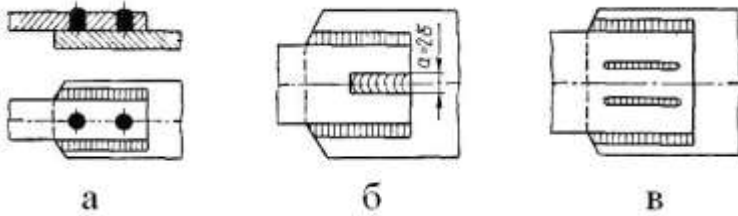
Коркові, прорізні та проплавні зварні шви
